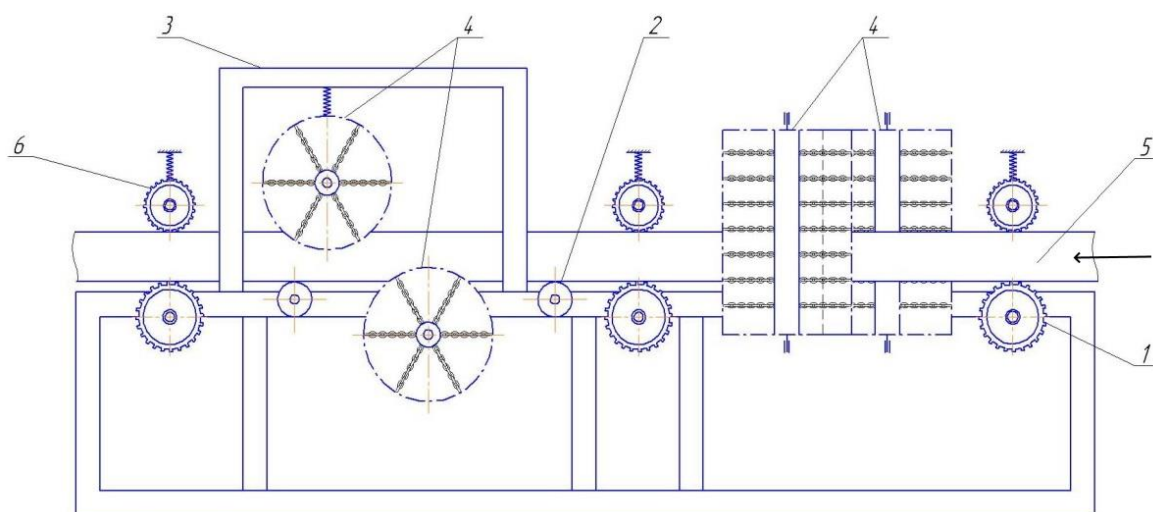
Вид с боку окорочного станка с ЦРО для обработки тонкомерных лесоматериалов: 1 – приводной вал системы подачи; 2 – поддерживающий ролик; 3 - рама; 4 – горизонтальные и вертикальные пары цеповых валов; 5 – обрабатываемый ствол дерева; 6 – прижимной валец.
